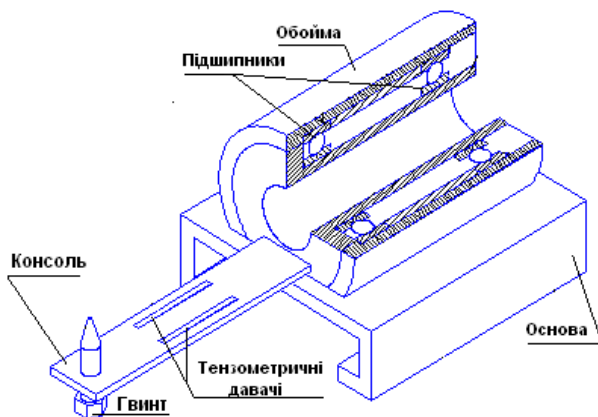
Принципова схема конструкції вузла вимірювання бокової сили притискування ОЦЕ і долота до стінок свердловини
